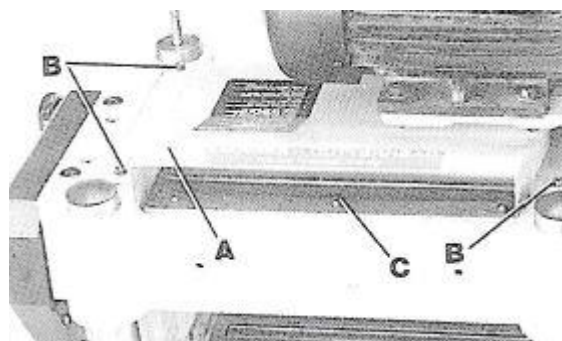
Сборка верхней крышки и лотка для сбора пыли
